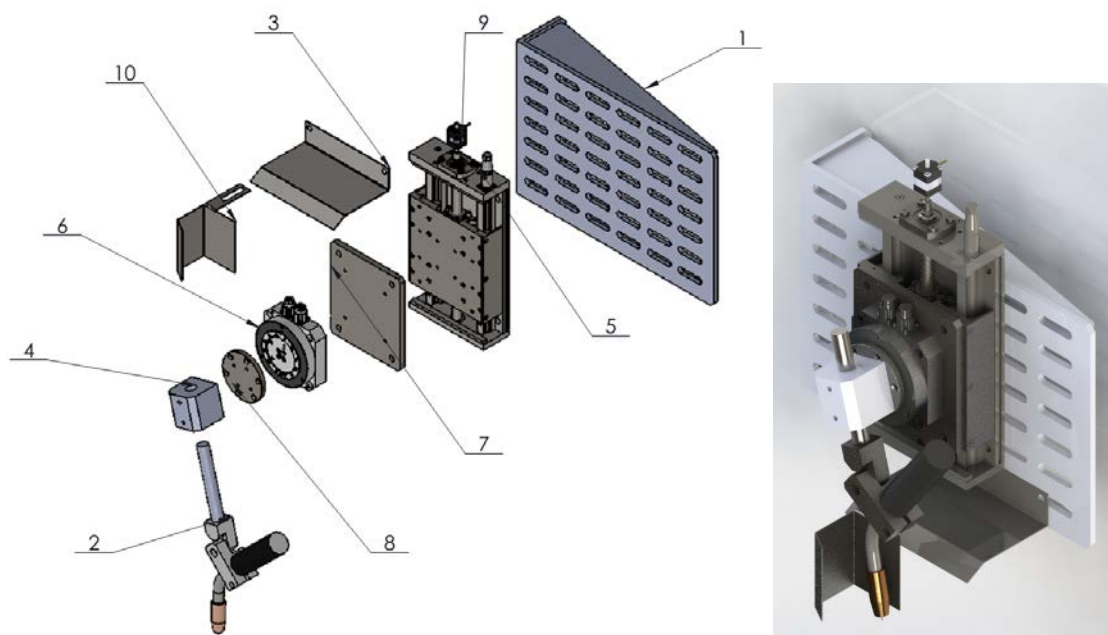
Mecanismo da tocha, representado em vista isométrica explodida e assemblada
